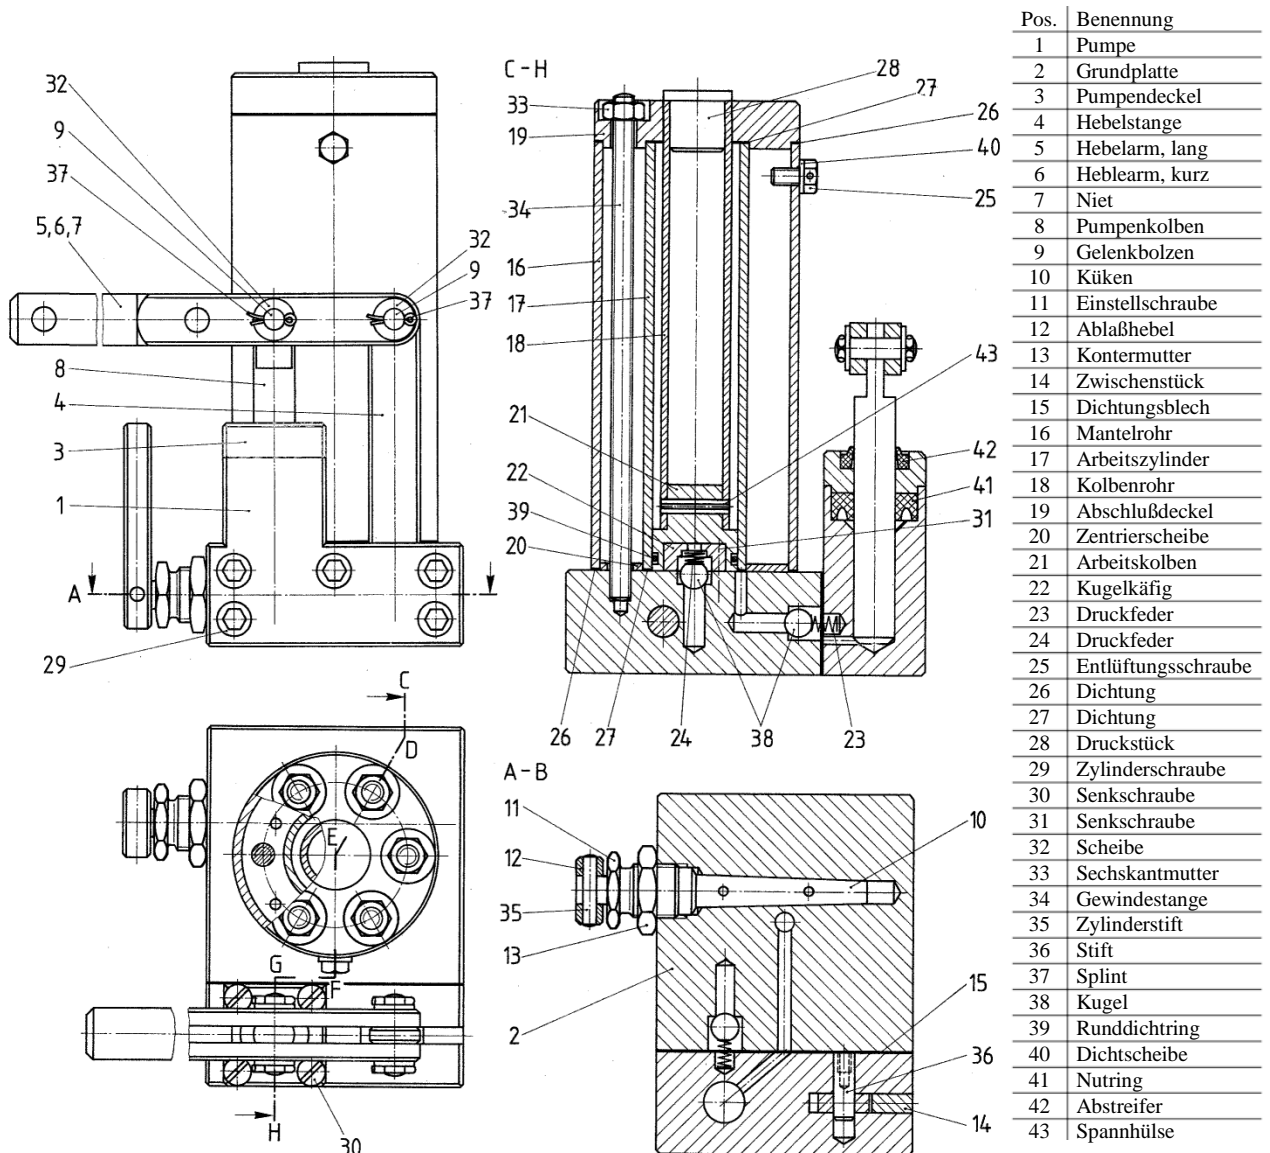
Baugruppenzeichnung "Hydraulikheber" /bay05/
